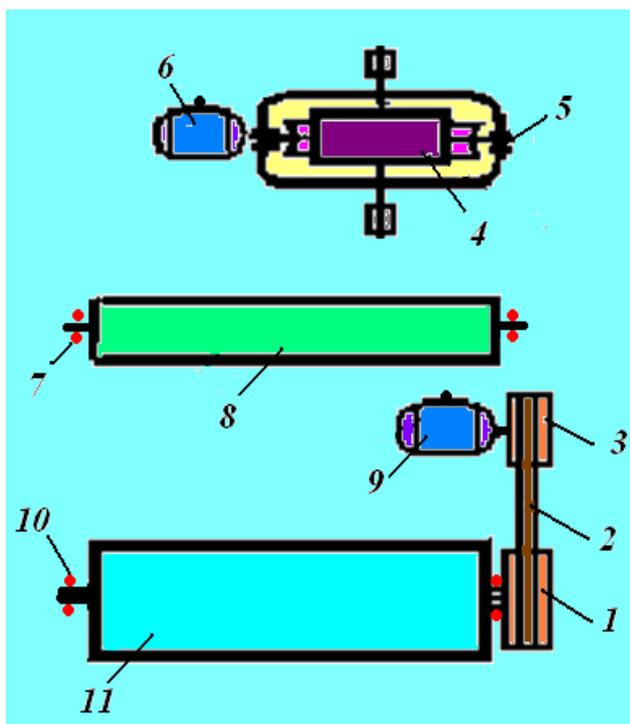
Кинематическая схема конвейера ленточного передвижного хлопкового КЛП-650:
